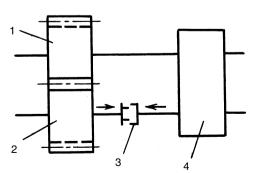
Принципиальная схема прибора для контроля кинематической погрешности зубчатых колёс
